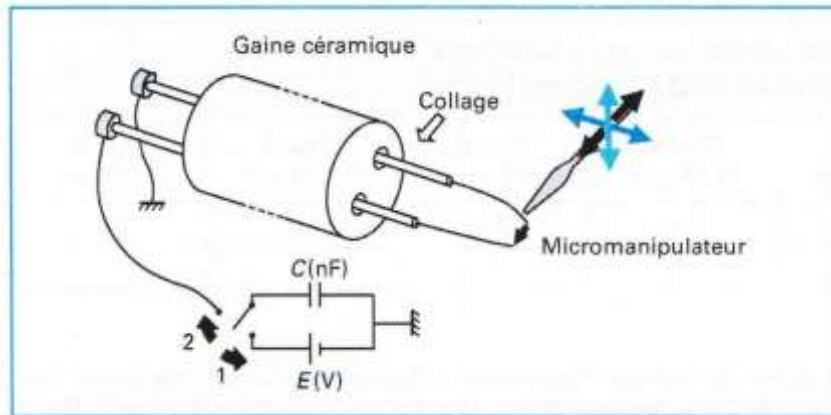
Technique de soudage des micro-thermocouples par décharge capacitive [47]
